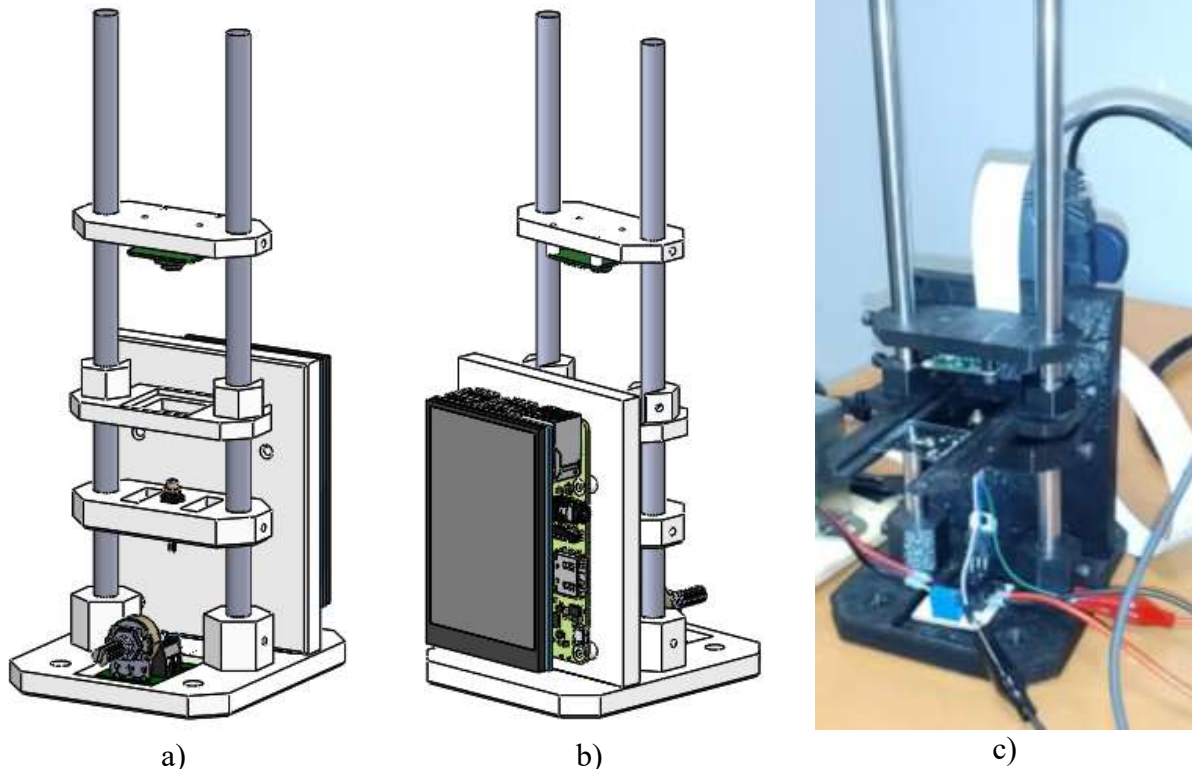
Ensamble de instrumento: a) CAD vista frontal isométrica, b) vista posterior isométrica y c) ensamble físico.
